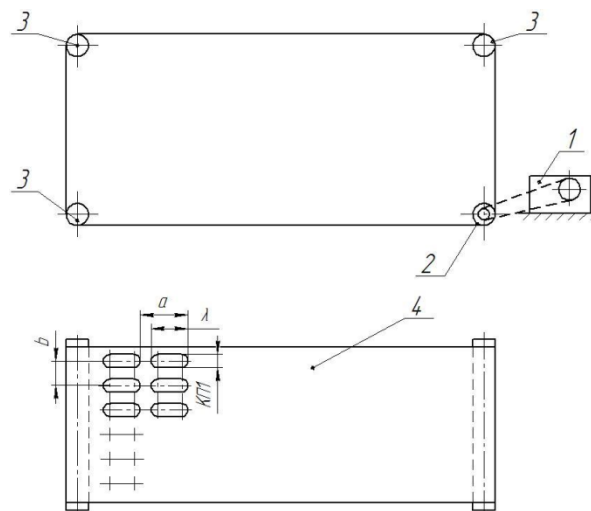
Схема встановлення калібрувального полотна з розмірами комірок: 1 – привід; 2 – ведучий барабан; 3 – підтримувальний барабан; 4 – транспортерна стрічка [2].
